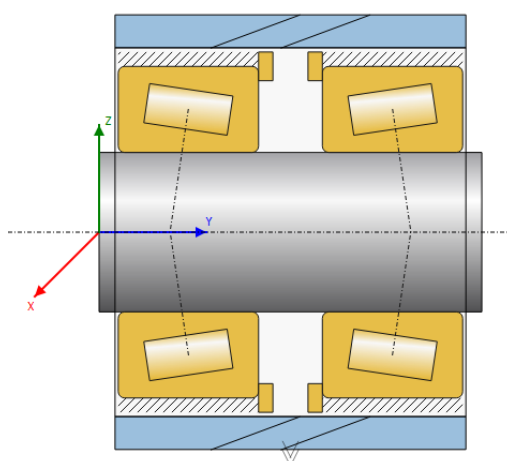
Расчетная модель первой паразитной шестерни несоосного редуктора
